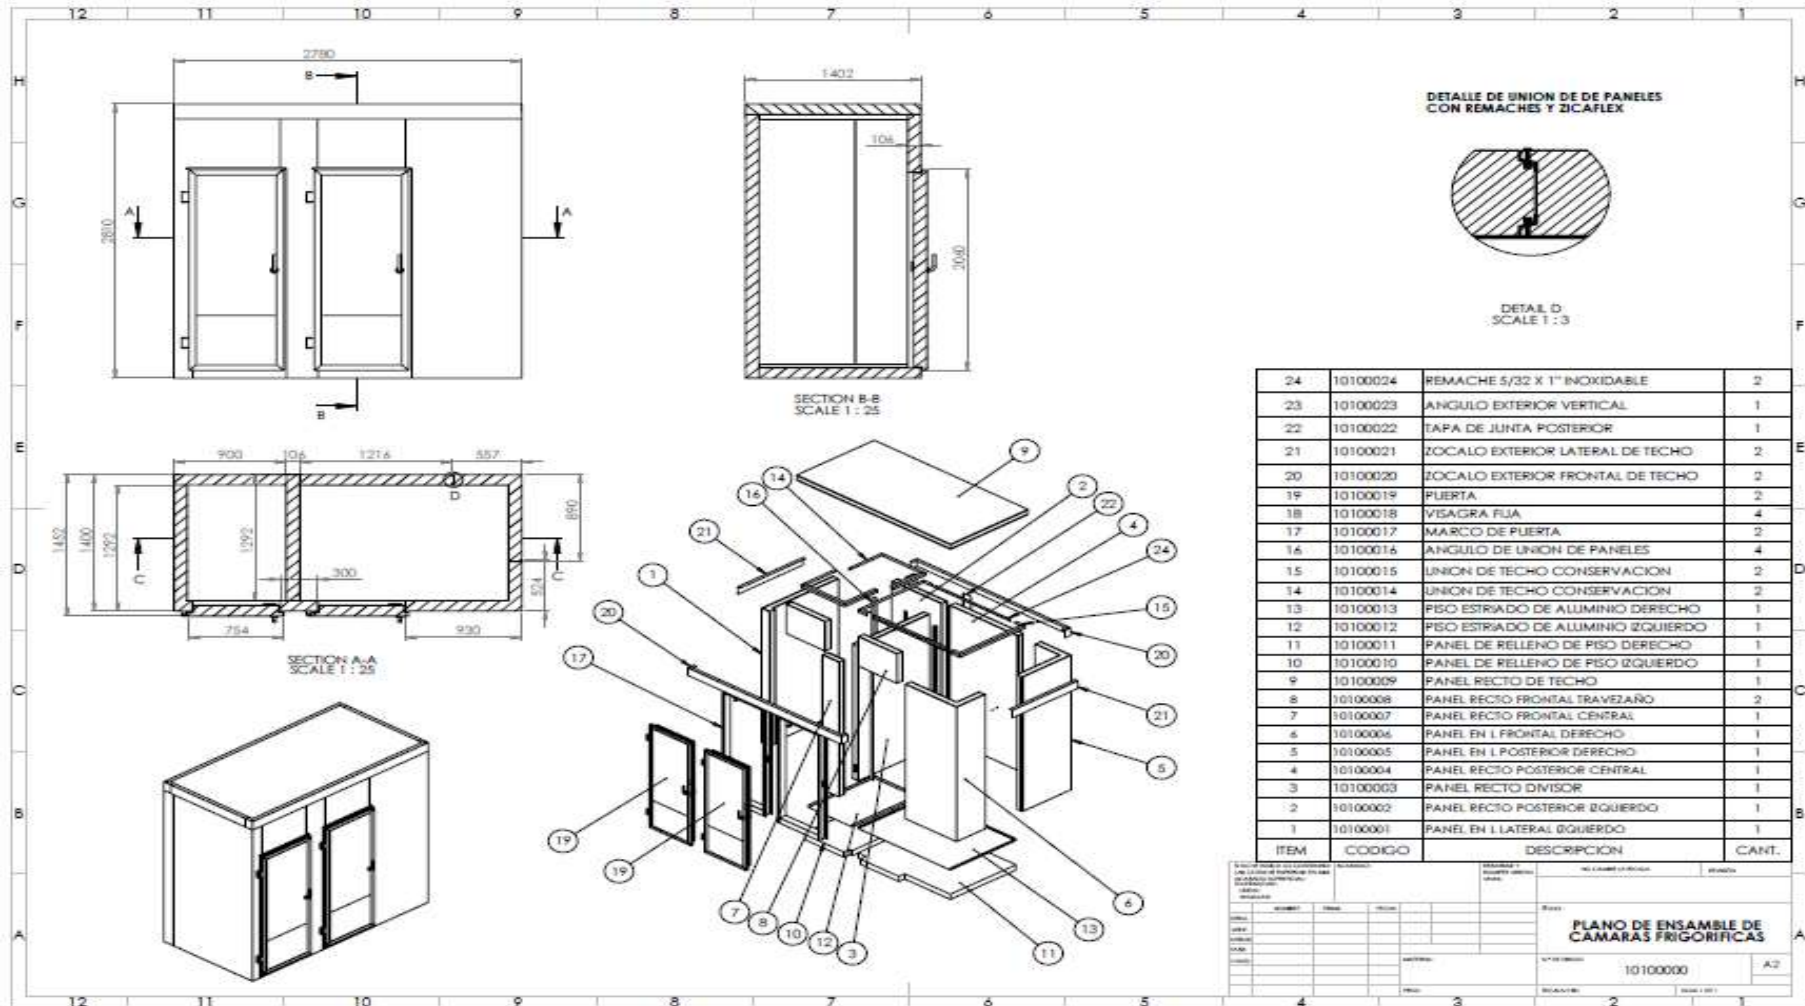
Plano de la máquina: Cámara Frigorífica. Plano mejorado con codificación. Fuente: Codem Tech Perú SAC.
